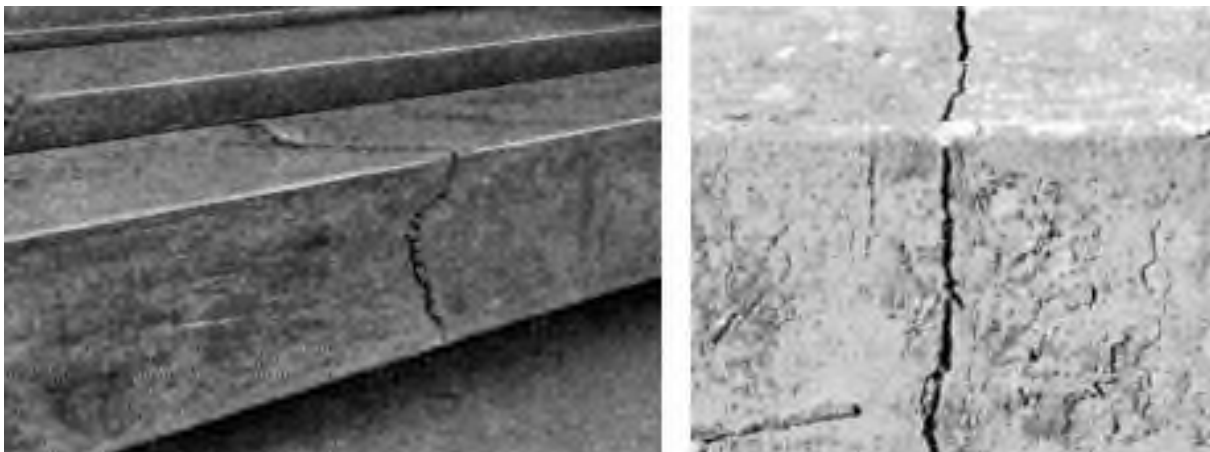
Пояс на поверхні безперервнолитої заготовки
